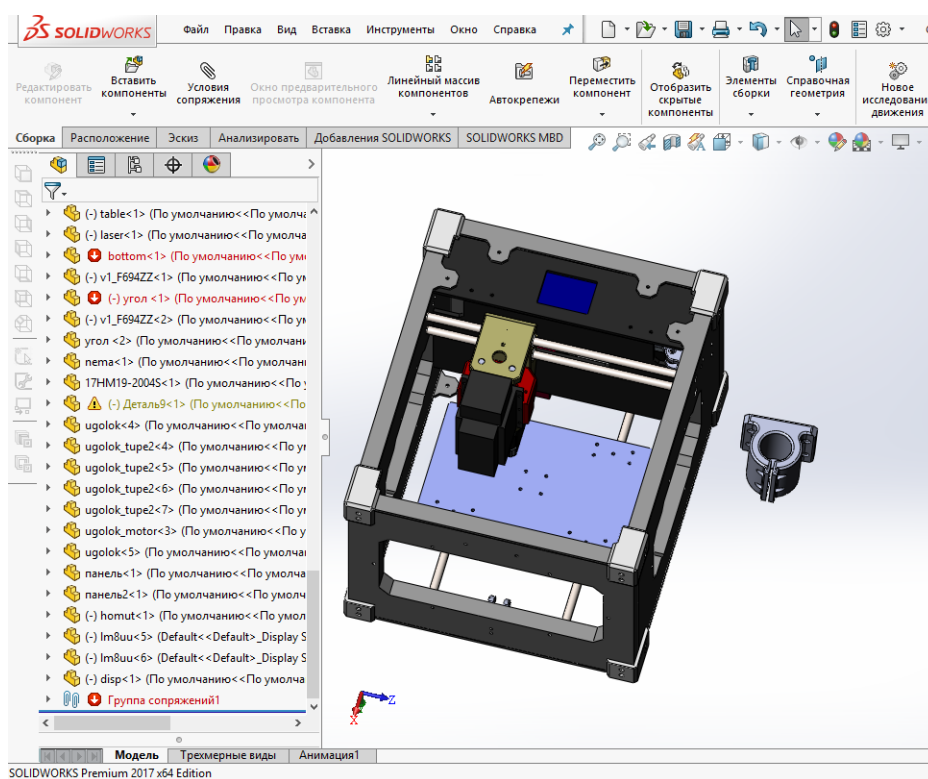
Модель корпуса станка и крепежа инструментальных модулей
